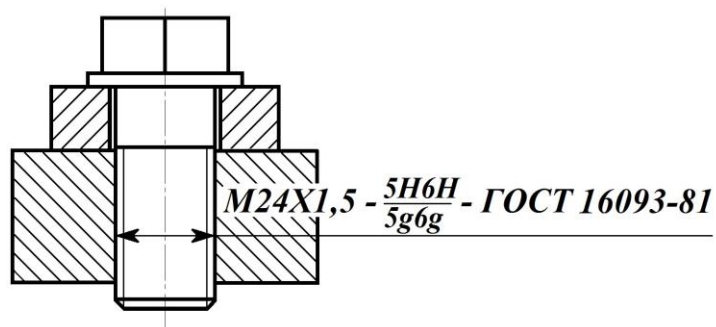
Обозначение резьбового соединения на сборочном чертеже (посадка с зазором)
